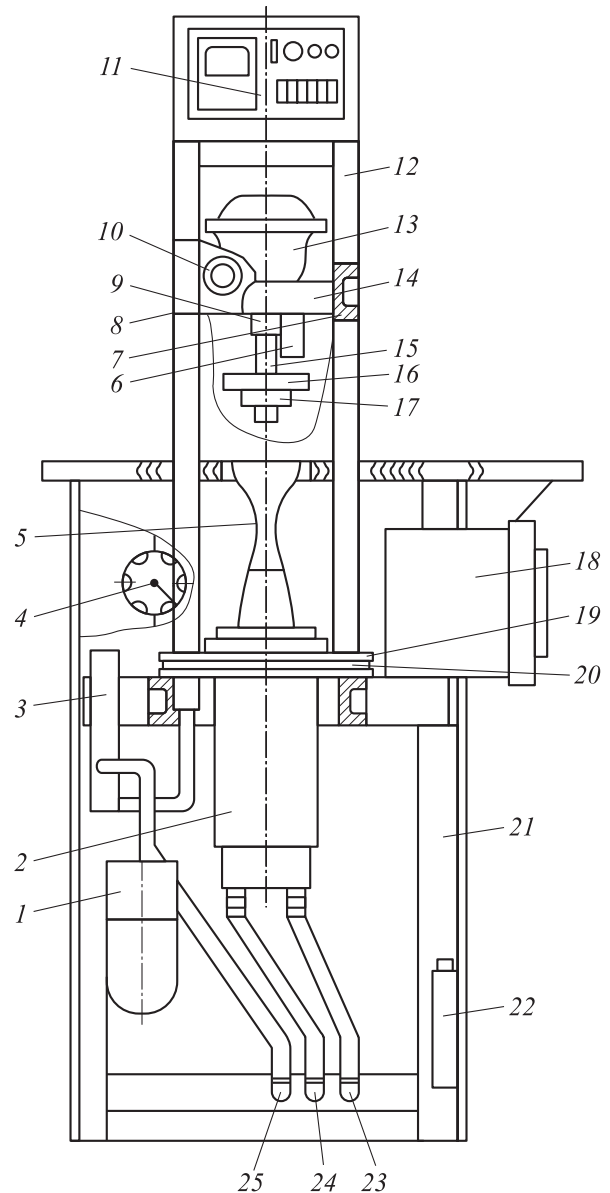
Схема сварочной машины для контурной УЗС колеса вентилятора из АБС-пластика
